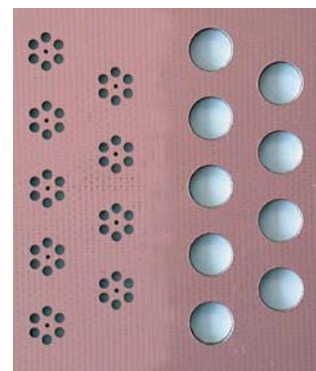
Пример рассверливания отверстий большого диаметра на заготовке печатной платы
